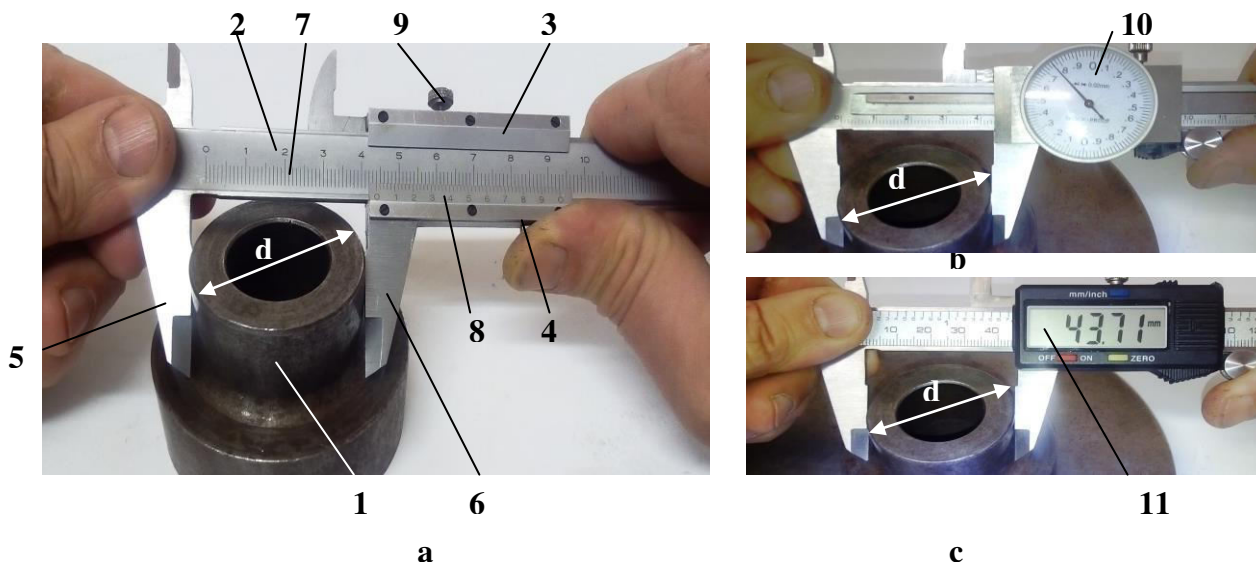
Măsurarea dimensiunilor exterioare cu șubler de exterior
